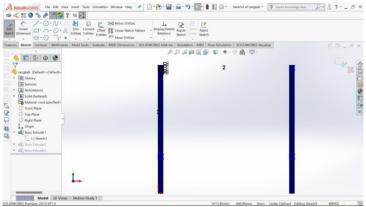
Desain 2 Dimensi Besi Hollow
